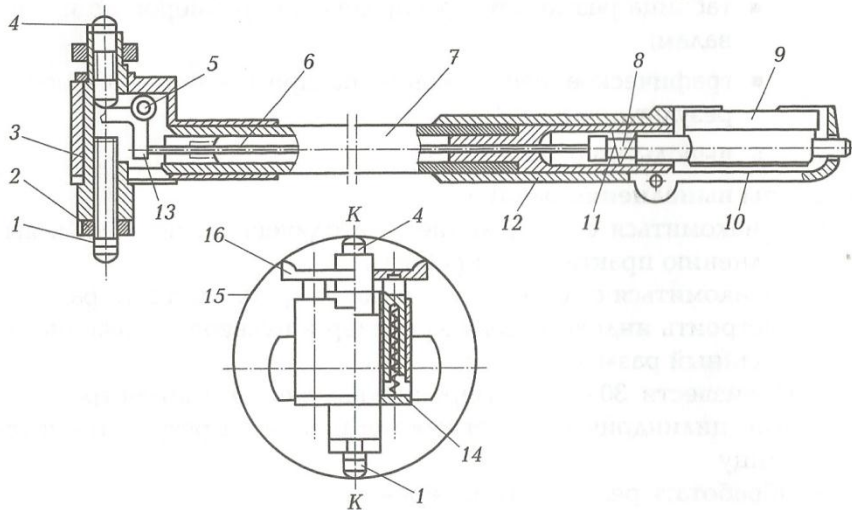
Конструктивная схема индикаторного нутромера:
